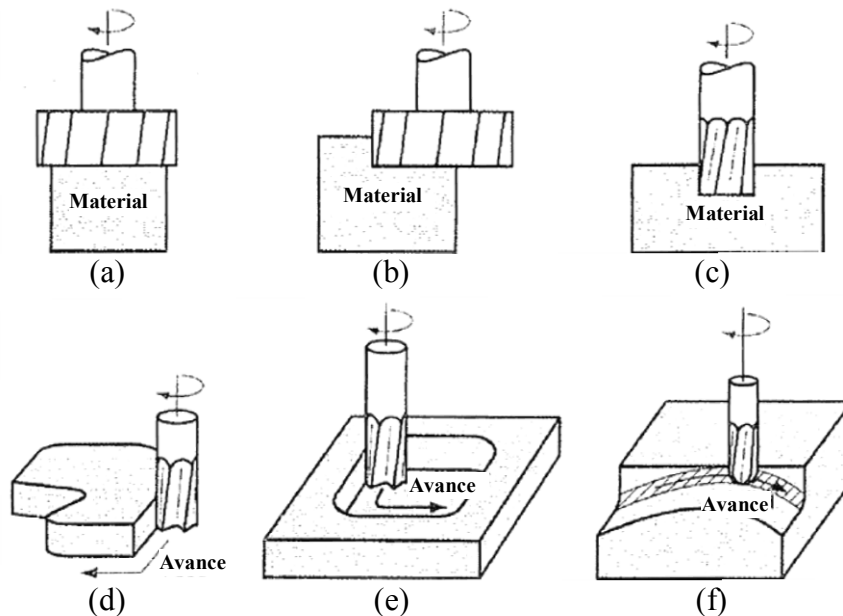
Maquinado frontal: a) maquinado frontal convencional, b) maquinado frontal parcial, c) maquinado terminal, d) maquinado de perfiles, e) maquinado de cavidades, y f) maquinado de contorno superficial.
